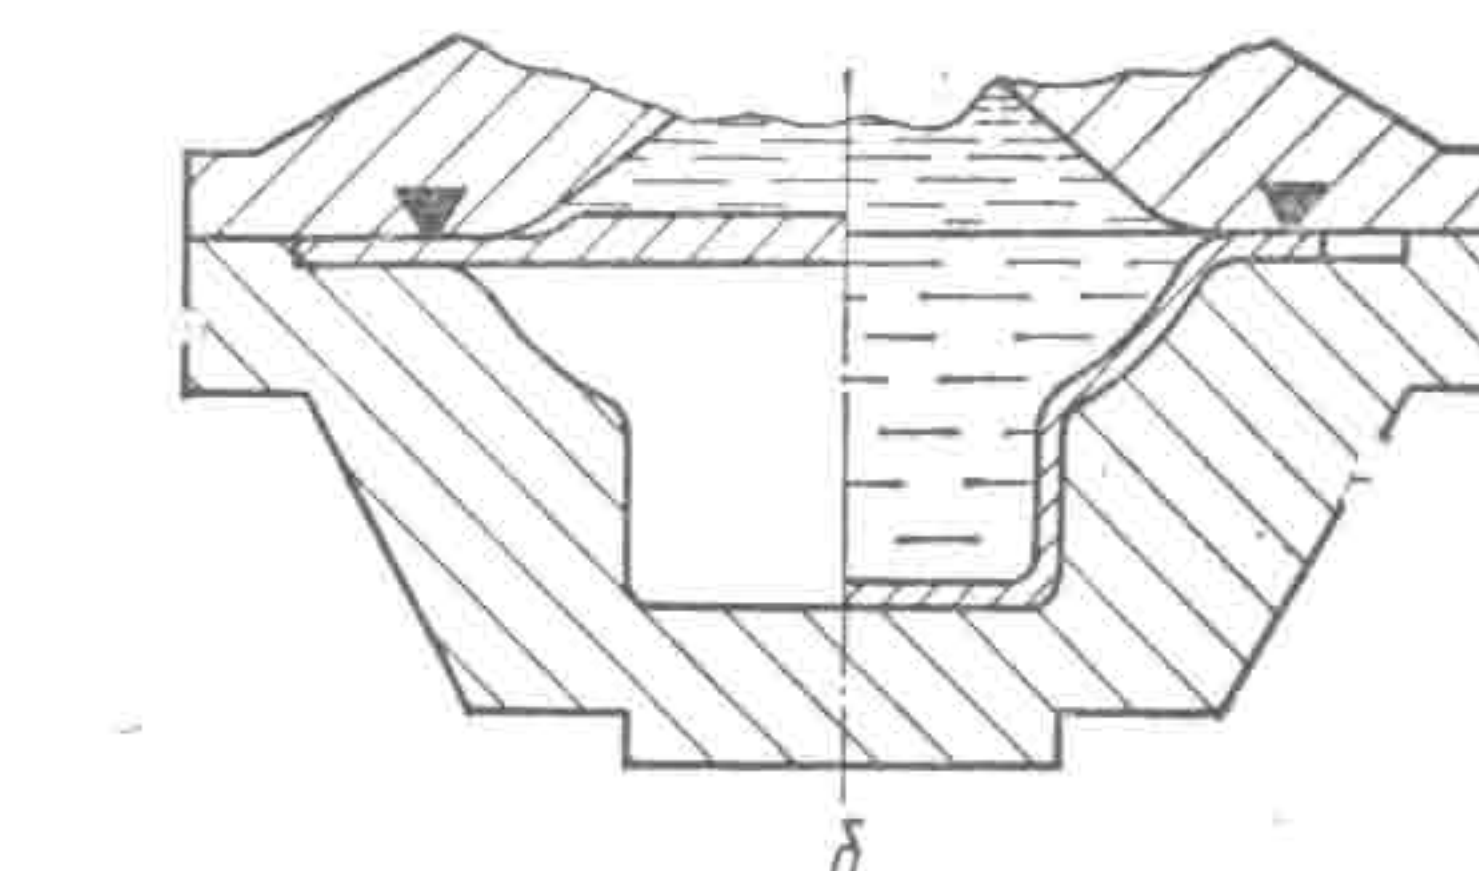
Экран, вытянутый на прессе Т1220 (а) по схеме вытяжки из разнотолщинной заготовки (б).
